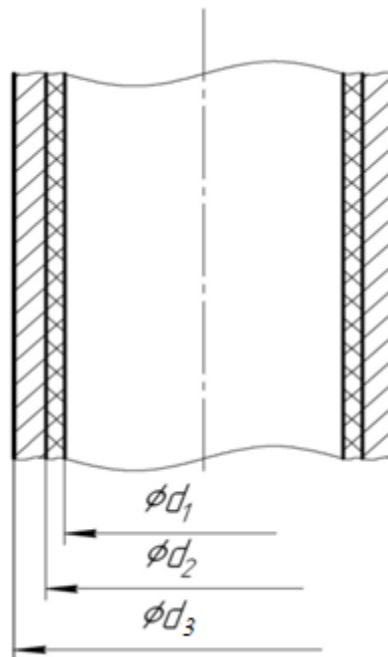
Схема циліндричної стінки змійовика котла з накипом
